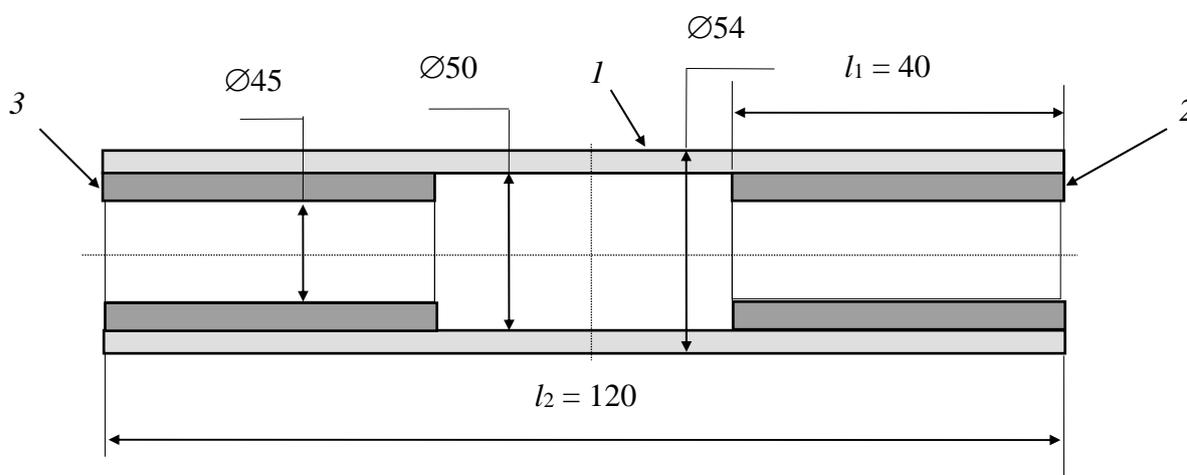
Эскиз заготовки из проката с обозначенными проходами обработки
